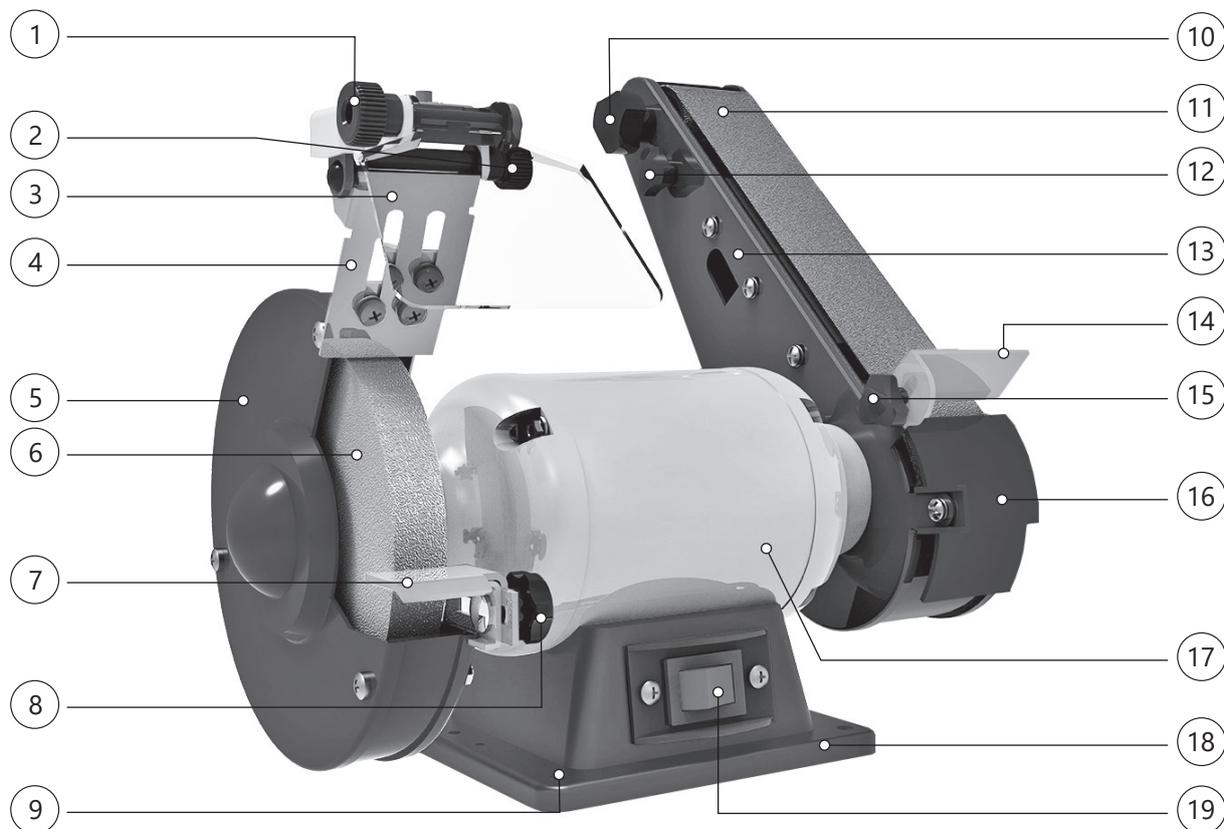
Основные элементы станка BELMASH MBG-150/50L.
